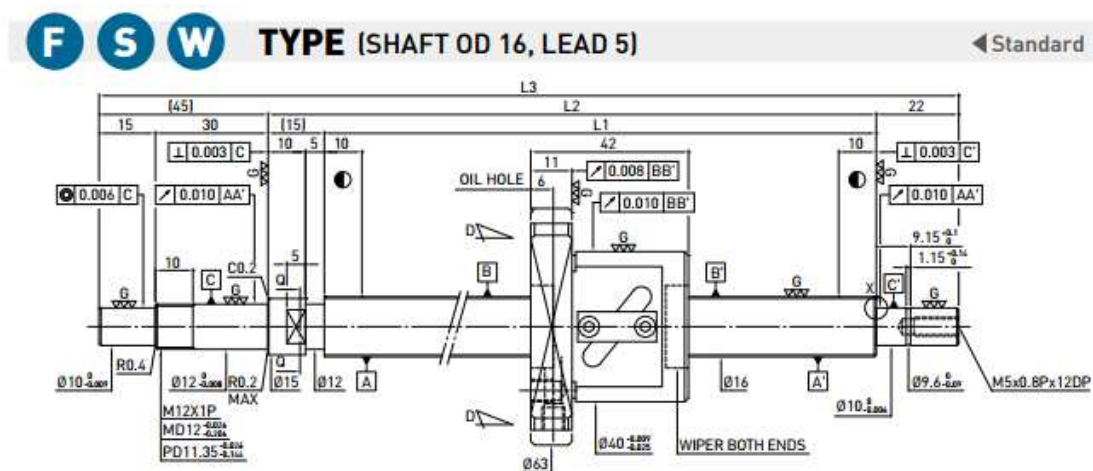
Tornillo de bolas FSW diámetro 16mm, paso 5mm
